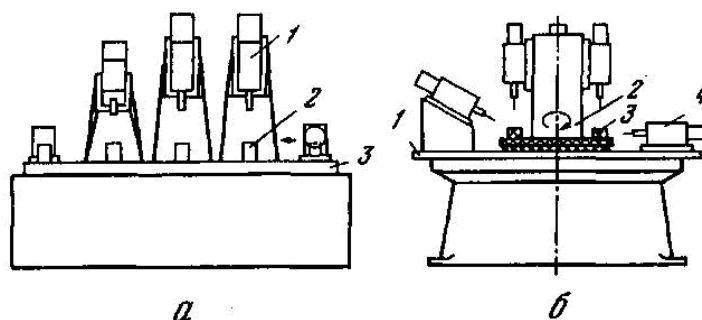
Компоновка агрегатних верстатів з прямолінійним переміщенням заготовок (а) і з центральною колоною (б)
